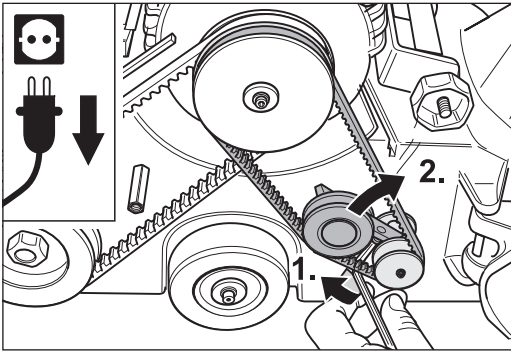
Die Klemmschraube des Riemenstellers lösen (1.) und den Keilriemen entspannen (2.).
